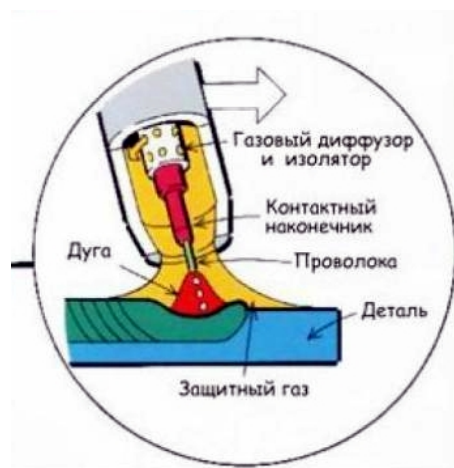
Схема механизированной сварки в среде защитного газа
